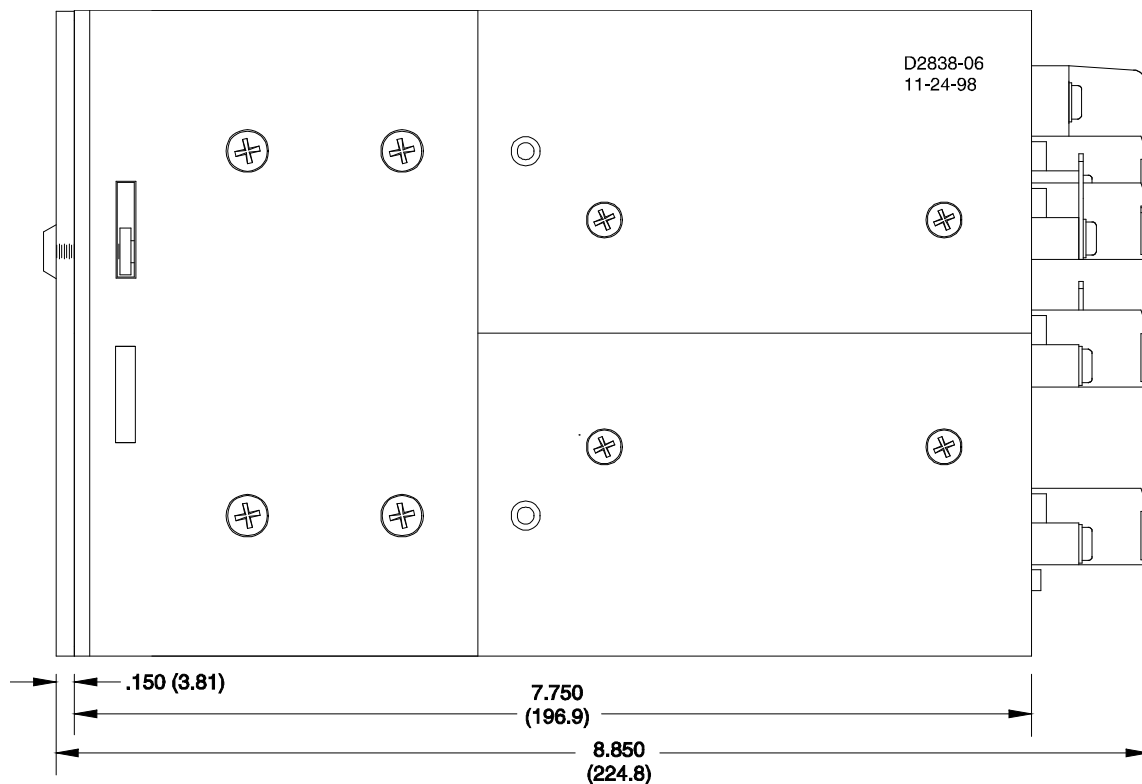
Dimensions du stabilisateur PSS-100 pour un montage en tiroir encastré, Vue de côté
